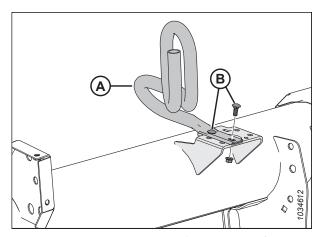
Nouveau guide de flexible installé sur la plateforme – Couteaux doubles D115 et D120
